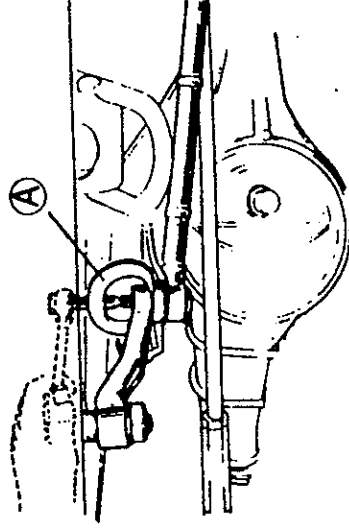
(A) Herramienta especial (Extractor del extremo de la barra de acoplamiento 09913-65210).
